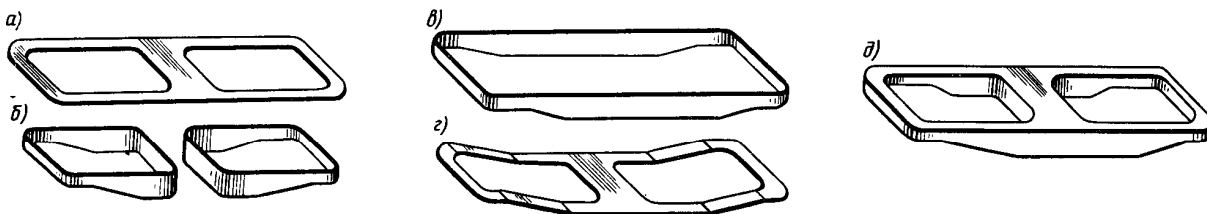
Сборочно-сварочные операции при изготовлении рамы тележки
